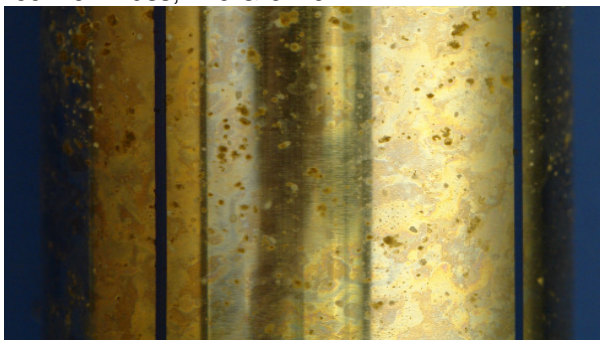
Lochfraß-Korrosion an einer Kolbenstange
